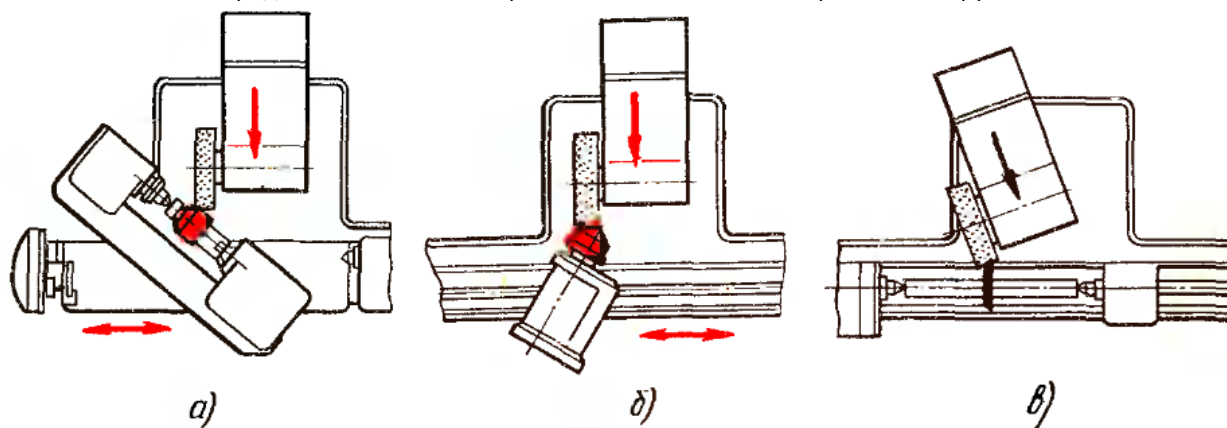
Схема наладки станка для шлифования поверхности с большой конусностью
